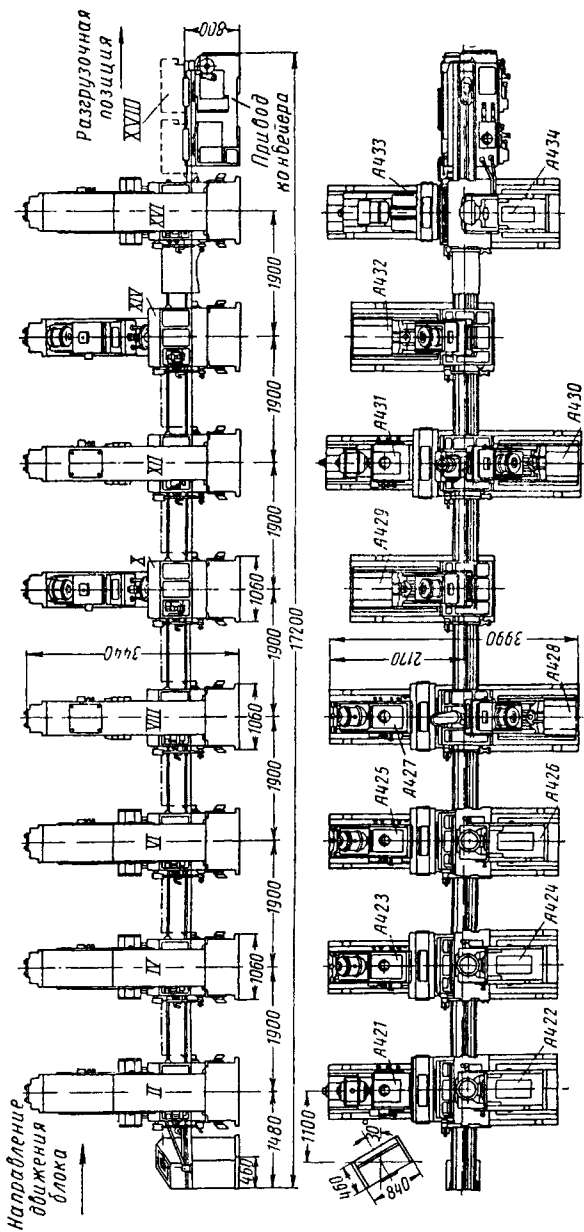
Участок автоматической линии для изготовления блока автомобильного двигателя
